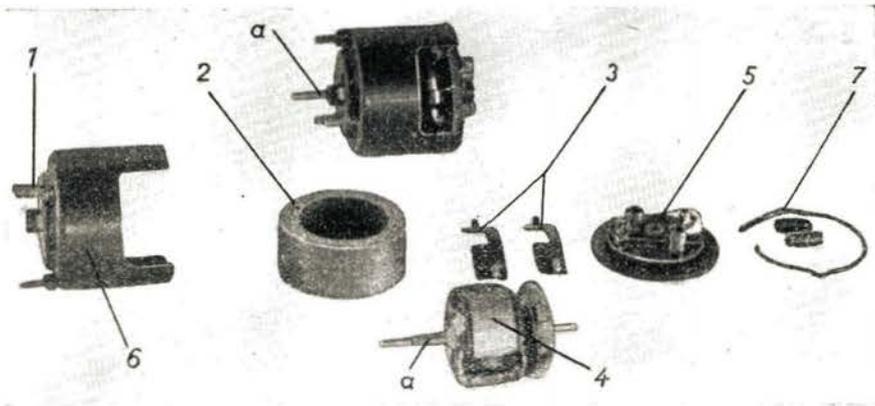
Einzelteile des Maniperm-Einbaumotors 1401. 1 Klemmring mit Druckschrauben, 2 Maniperm-Ringmagnet, 3 Distanzstücke, 4 Motoranker, 5 Bürstenbrücke, 6 Motorgehäuse, 7 Sicherungsring, a abgesetzte Ankerachse
